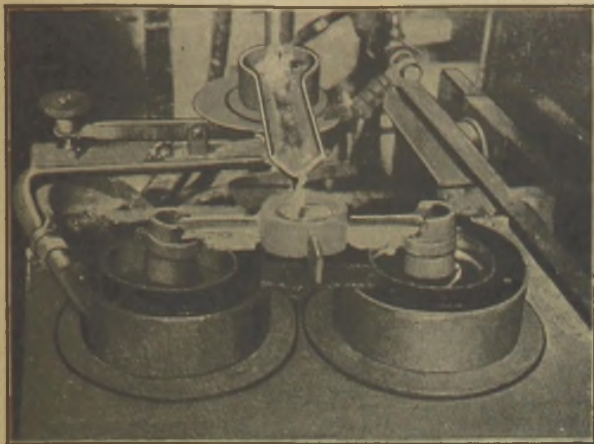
Vollkontinuierlicher Zweistrangguß. Kurzkokille mit Metallzuführung.
